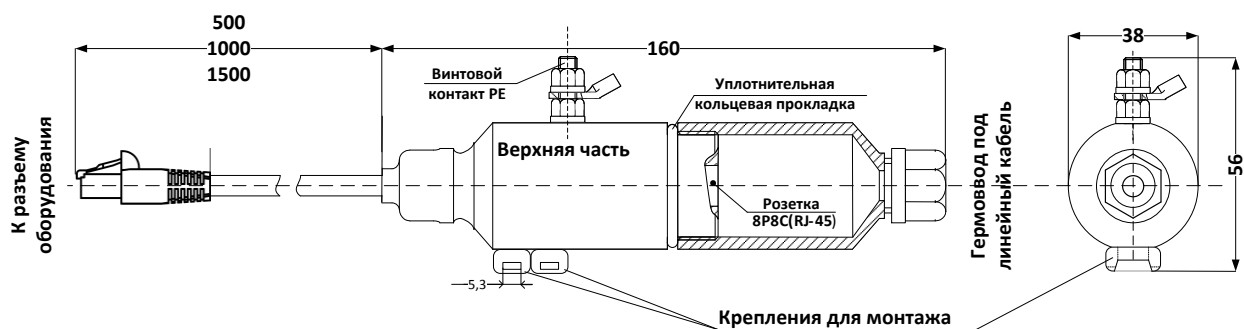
Габаритные размеры устройства FEP M f/m OD
